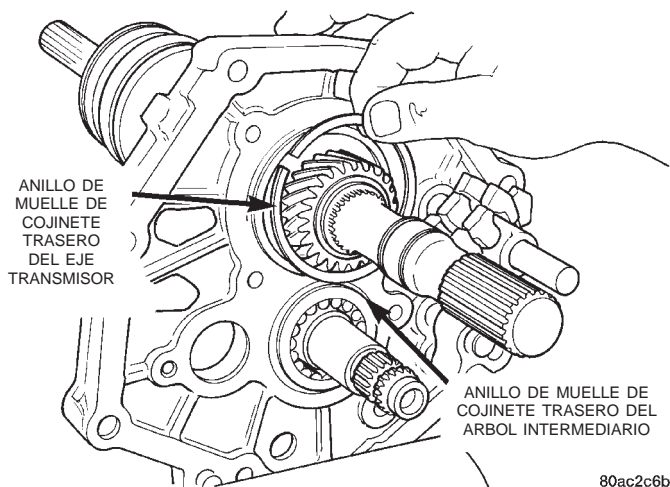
Desmontaje de anillo de muelle de cojinete trasero del eje transmisor
